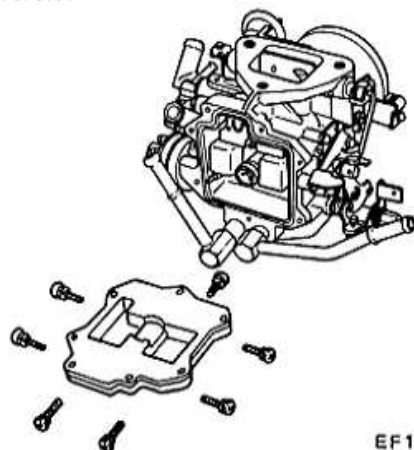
Démontage du couvercle de cuve à niveau constant
